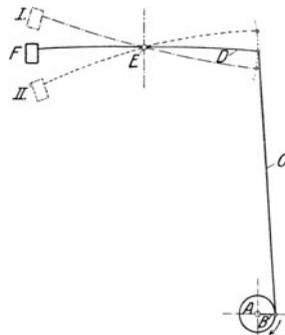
Die Wirkung einer Feder im Hebelhammer.
